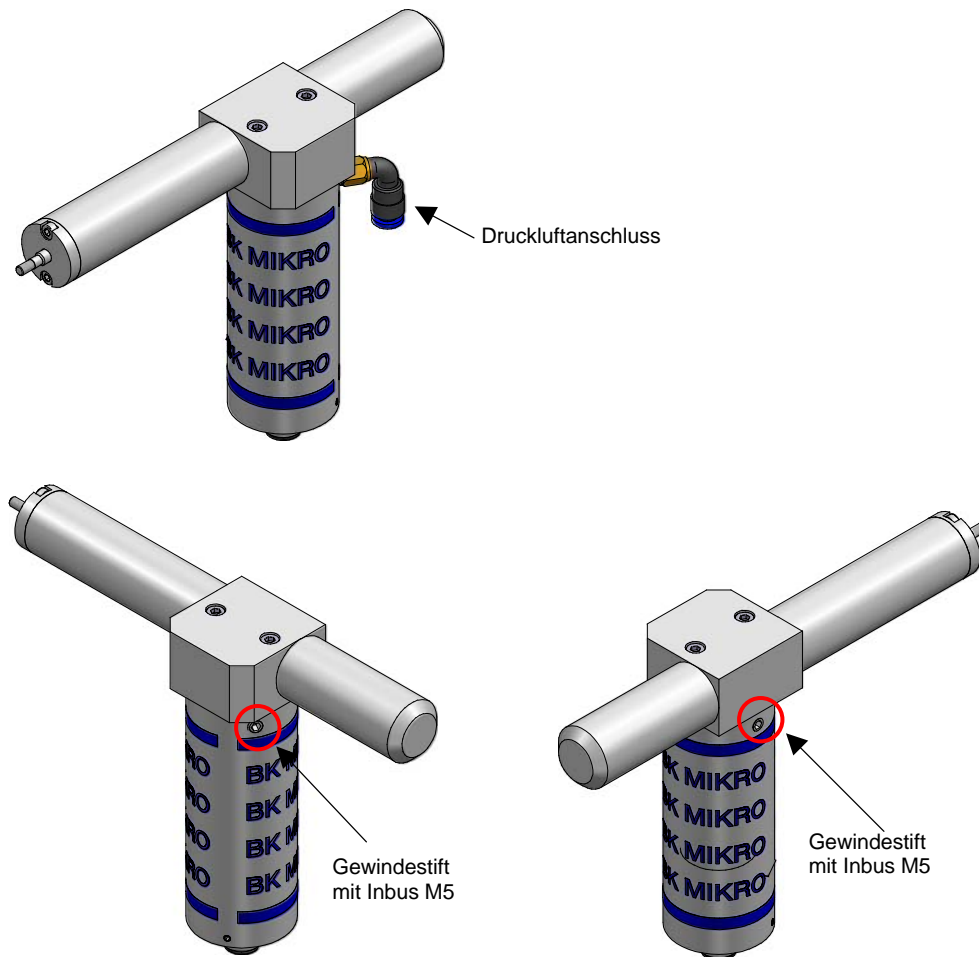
Option: Druckluftausgleich TK9LIN50/100
